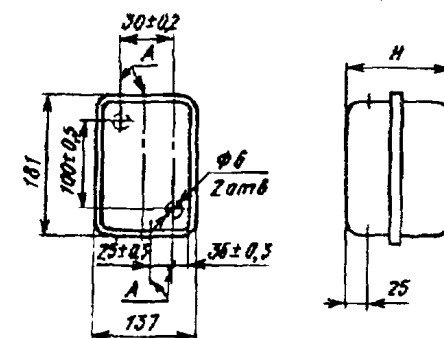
Габаритные, установочные размеры пускателей типа ПМ12-010 реверсивных в оболочках степени защиты IP40
